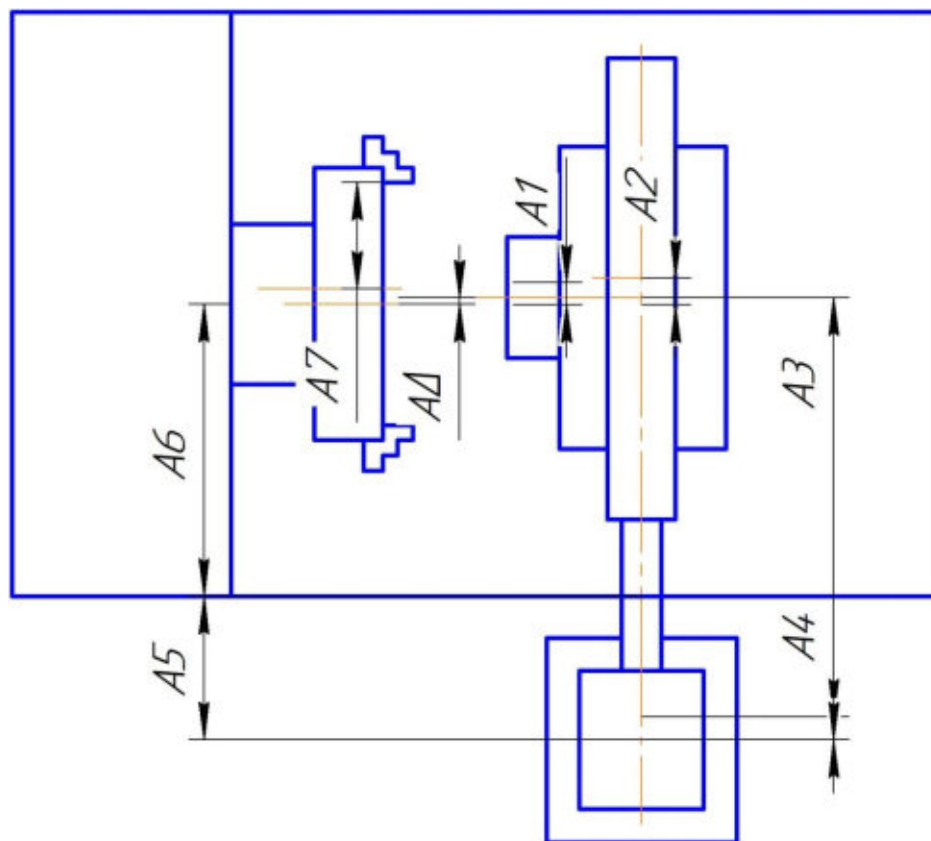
Схема размерных связей при автоматической загрузке токарного станка
